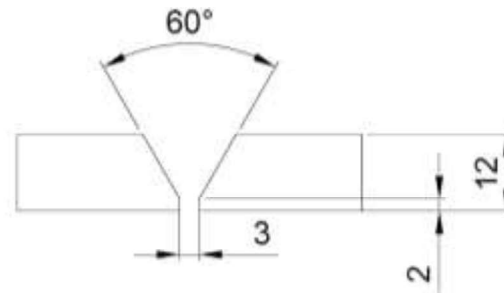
Diseño de la junta para soldadura con medidas en milímetros.
